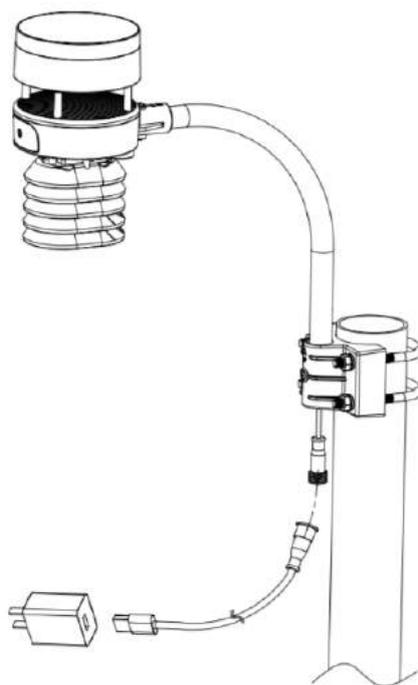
Schema di montaggio del pacchetto del sensore 5-5
